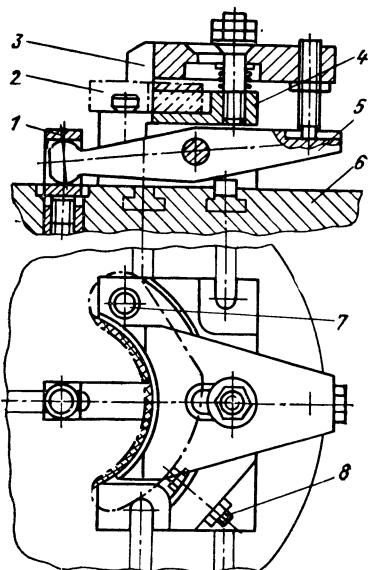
Сменная наладка на круглый стол для фрезерования контура скобы на вертикально-фрезерном станке
